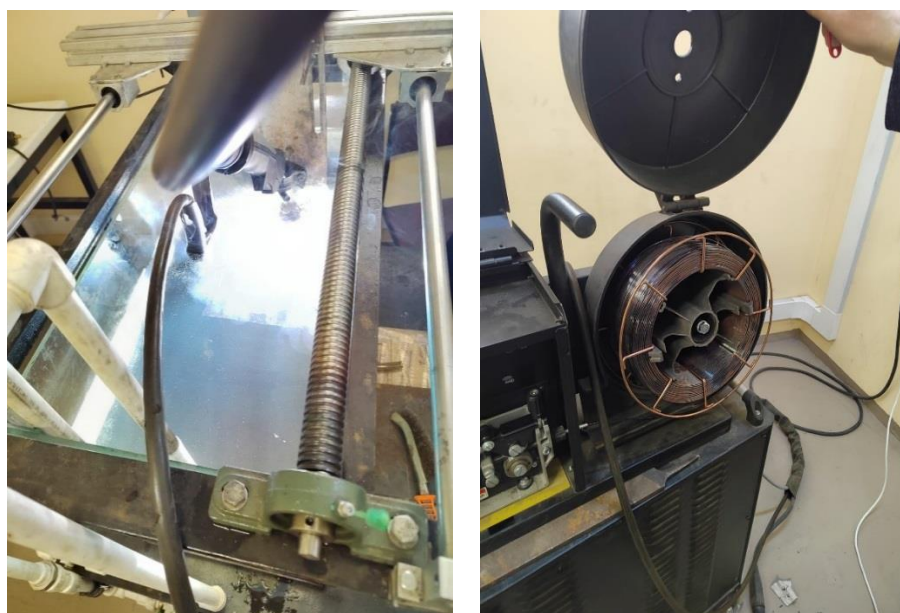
Внешний вид стенда для подводной сварки
